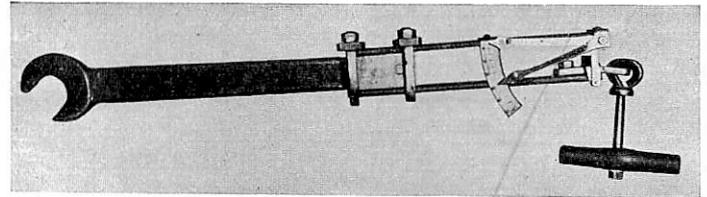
Schraubenschlüssel der Technischen Hochschule Karlsruhe.
